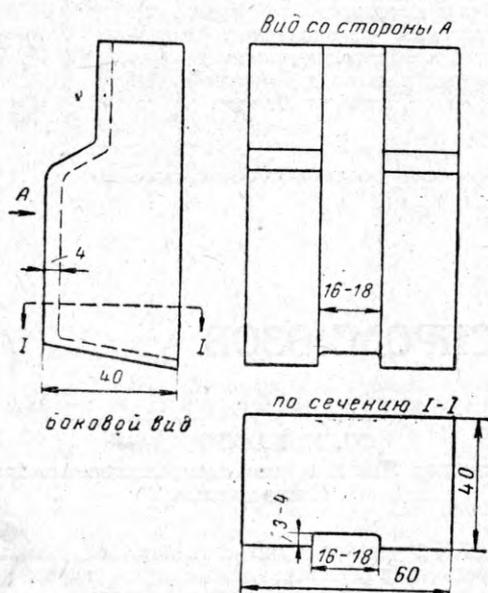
Форма и размеры медных боковых полуформ для сварки стыков узкоколейных рельсов типа Р18
